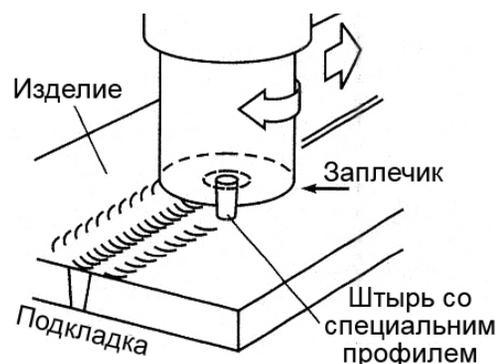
Схема процесса сварки трением с перемешиванием
